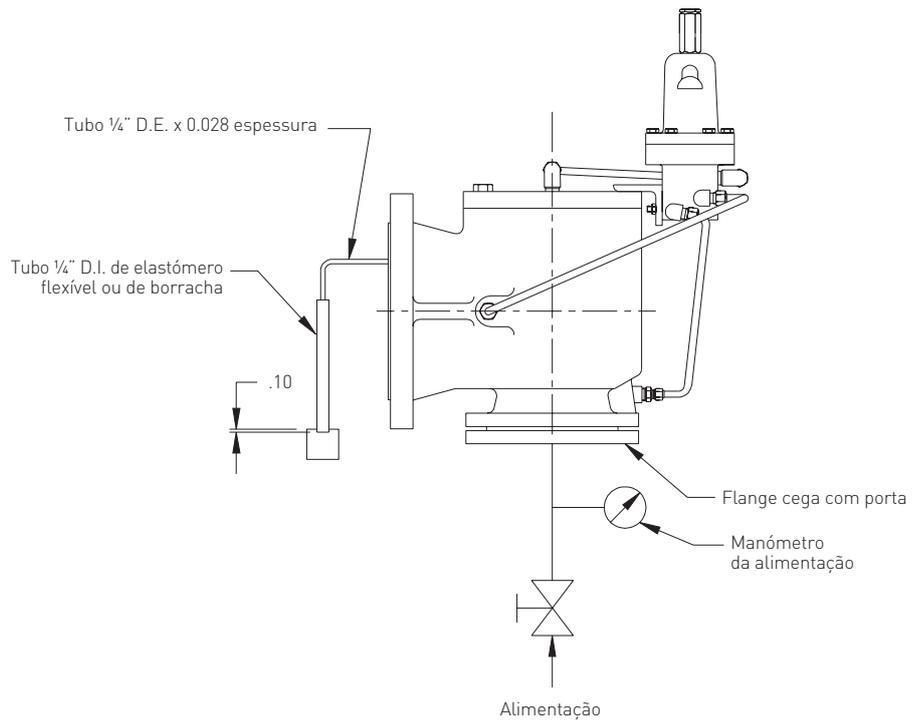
DISPOSITIVO DE ENSAIO PARA VÁLVULAS COM PILOTO STANDARD
